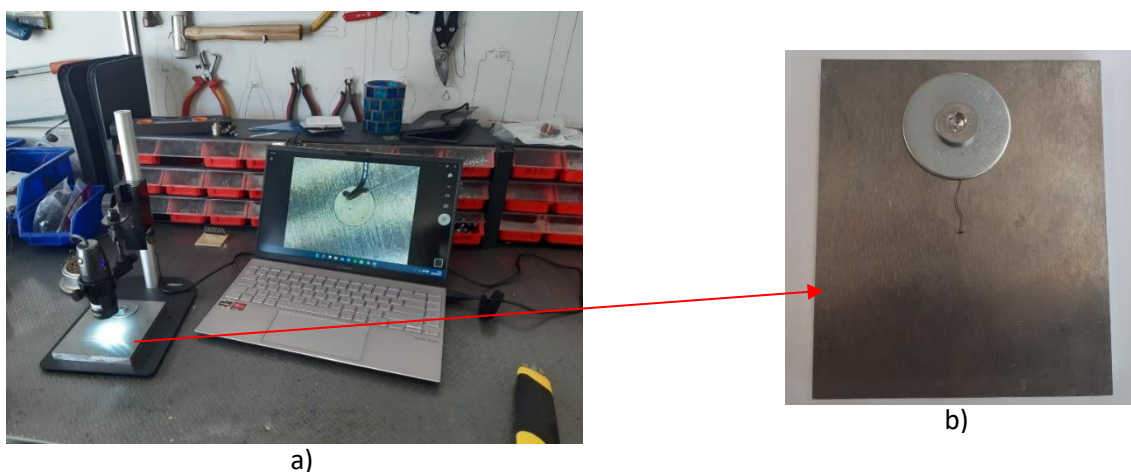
Configuração de soldadura a) Local de soldadura b) Base de soldadura
